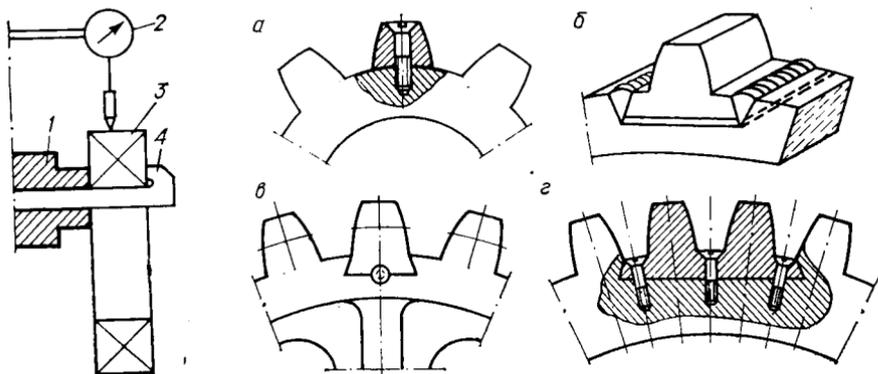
Схема приспособления для контроля подшипников качения: 1 — упор; 2 — индикатор; 3 — подшипник; 4 — насадка.
